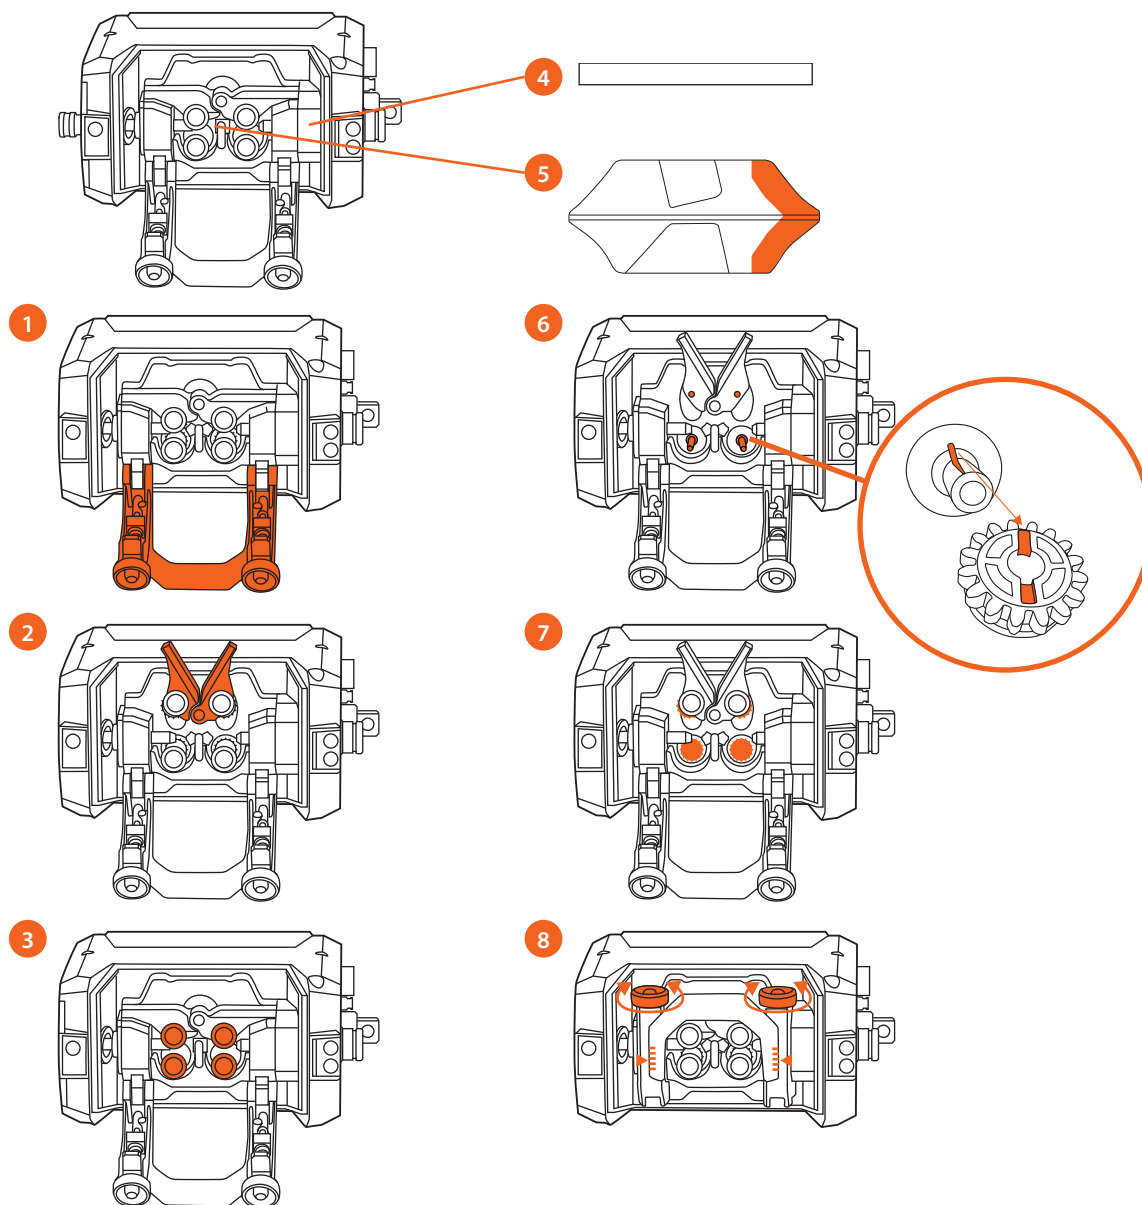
Установка направляющих трубок и подающих роликов
